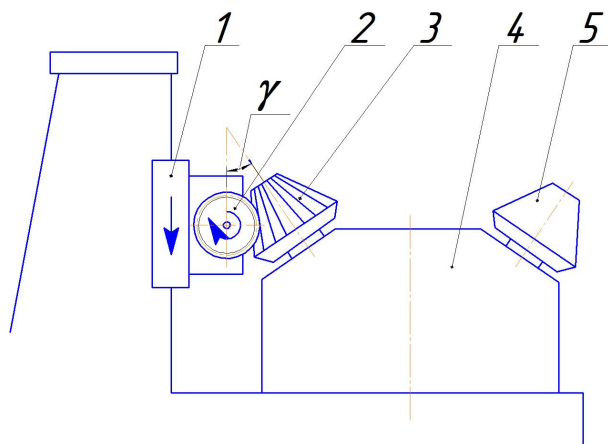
Двухпозиционный зубофрезерный полуавтомат для нарезания зубьев конических колес
